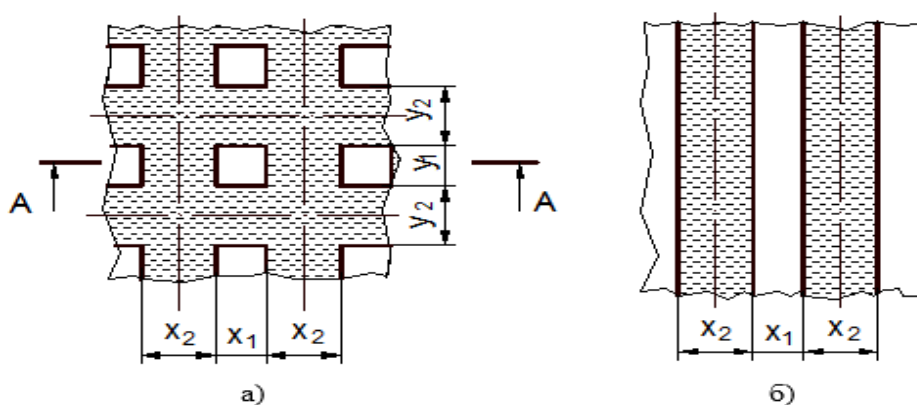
Варіанти реалізації рельєфу (вид зверху) нанесеного на пластинах біметалу:
